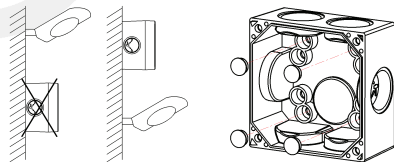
Встановлення ковпачків для отворів кріплення верхньої частини корпусу:
